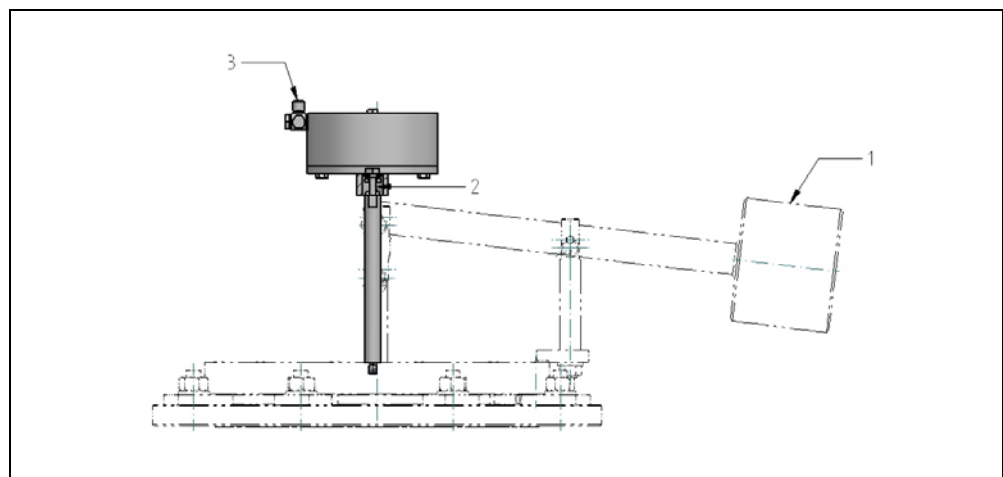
Esquema con dispositivo de levantamiento DN 300 – DN 400
